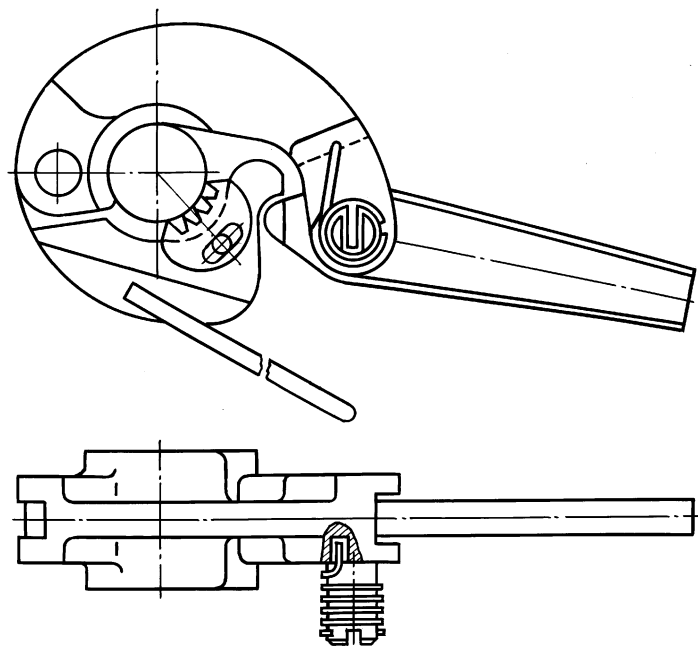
Ключ трубный двухшарнирный КТДР-73
